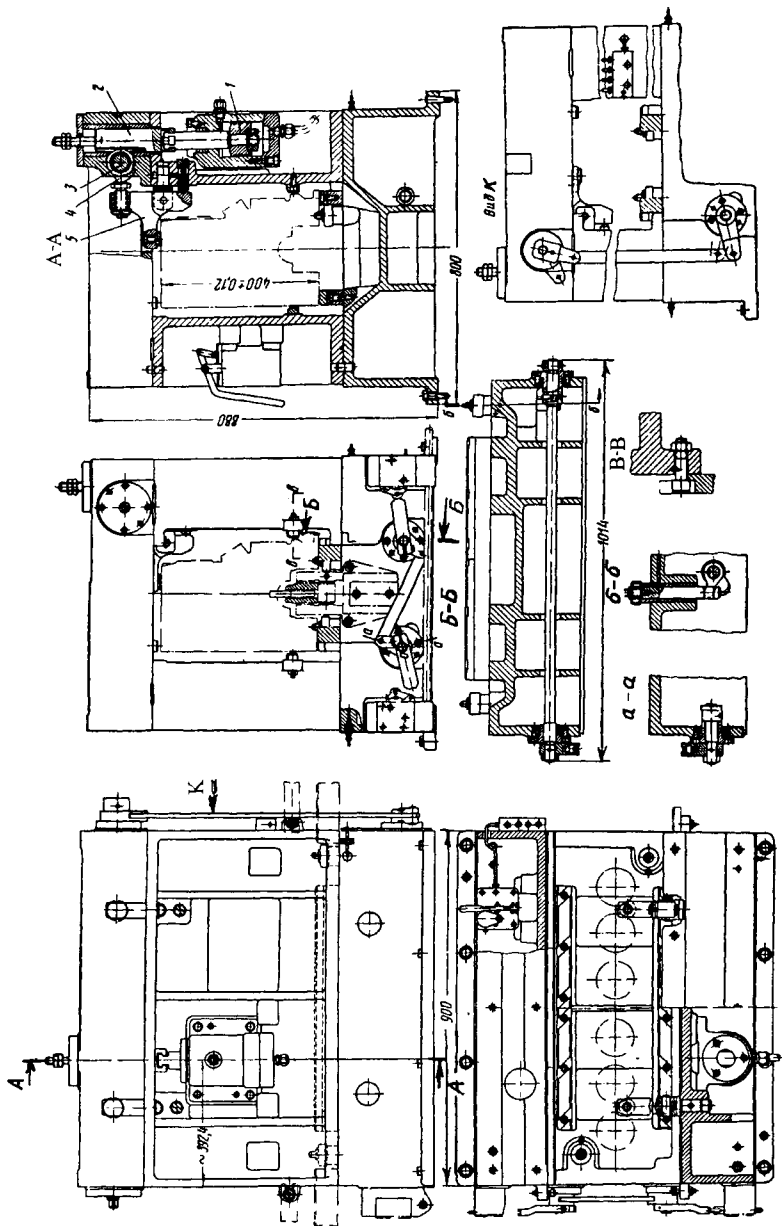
Приспособление, используемое для базирования и закрепления заготовки блока двигателя на позициях автоматической линии
